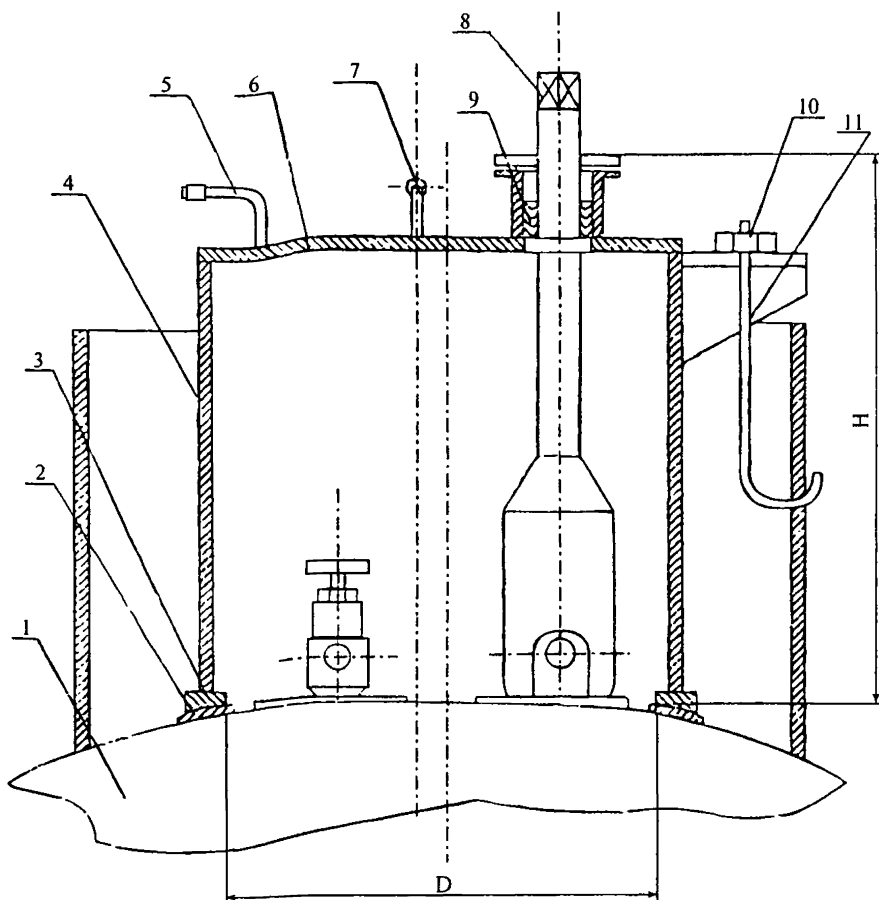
Устройство для эвакуации хлора из дефектных контейнеров И61-0564.000, И61-0568.000: 1 – корпус контейнера; 2 – уплотнительная прокладка; 3 – фланец; 4 – обечайка; 5 – отводящий патрубок; 6 – днище; 7 – патрубок для манометра; 8 – ключ; 9 – сальниковая камера; 10 – гайка; 11 – анкерная тяга
